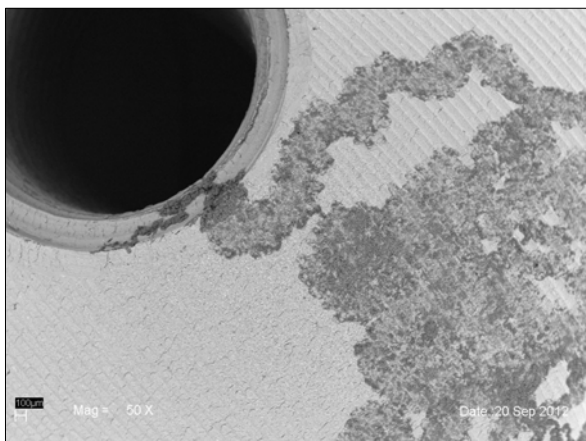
Korrosionsspur ausgehend von einer Bohrung im Bauteil (REM-Aufnahme)
